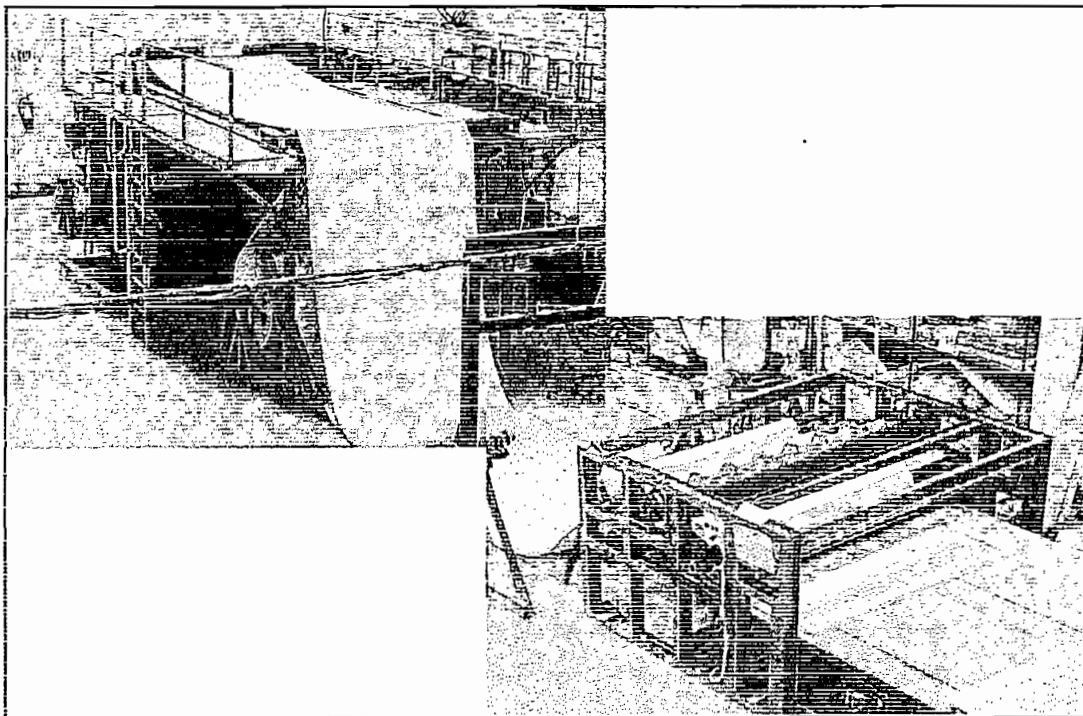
Vista de las máquinas corrugadora y cortadora<sup>5</sup>.
